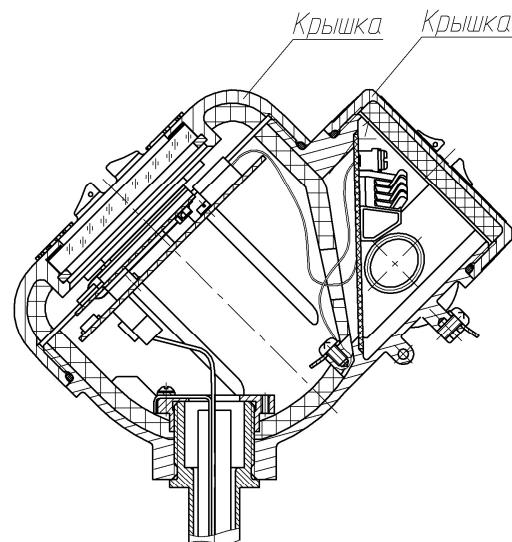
Габаритные размеры приборов (лист 4)
